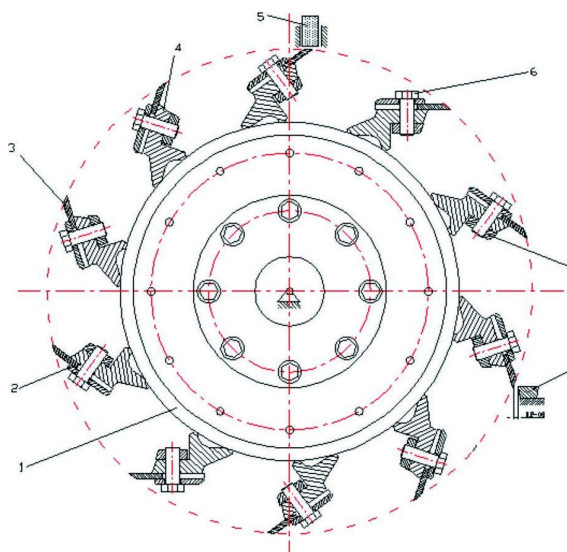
Схема расположения ножей (одно кольцо), заточного устройства и противорежущего бруса измельчающего аппарата кормоуборочного комбайна
